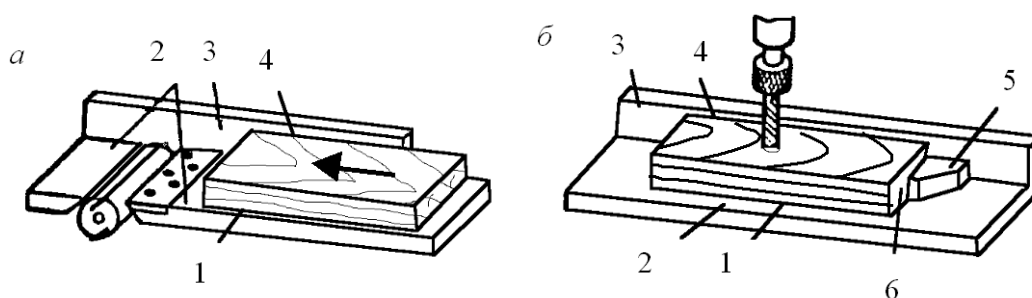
Базирование детали: а – подвижное; б – неподвижное
